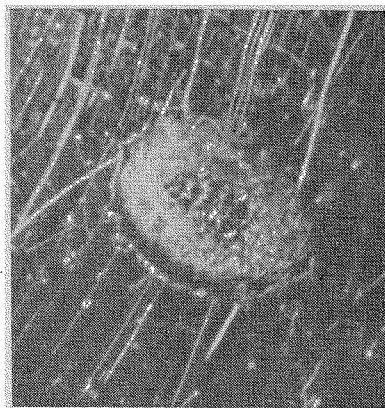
Отпечаток сварочного наконечника на детали при паличии приваривания
